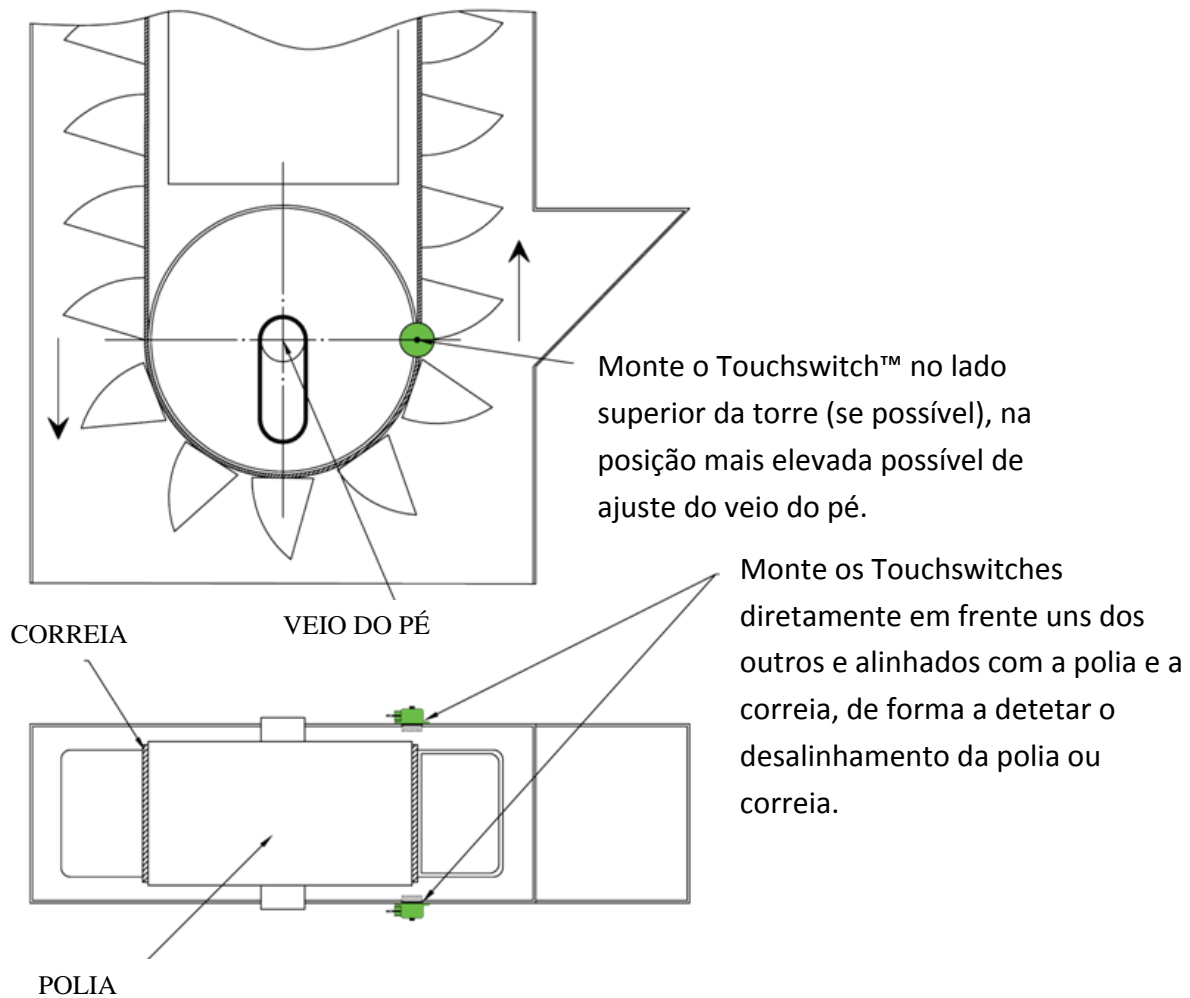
Posições de montagem do Touchswitch – Polia inferior
